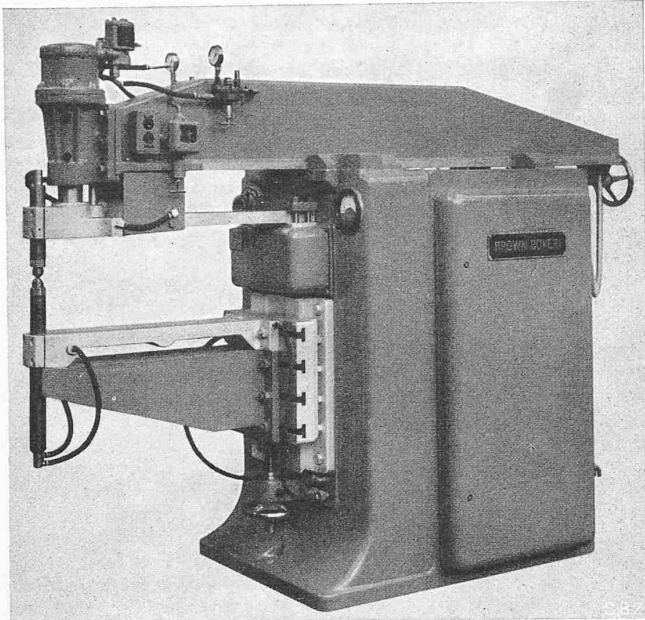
Druckluftbetätigte Brown-Boveri-Punktschweissmaschine, speziell zum Verschweissen von Aluminium, mit einstellbarer Fensteröffnung. Stufenlose Regulierung des Schweißstromes, der Schweisszeit und des Elektrodendruckes bürgt für wirtschaftliche und zuverlässige Schweissung
